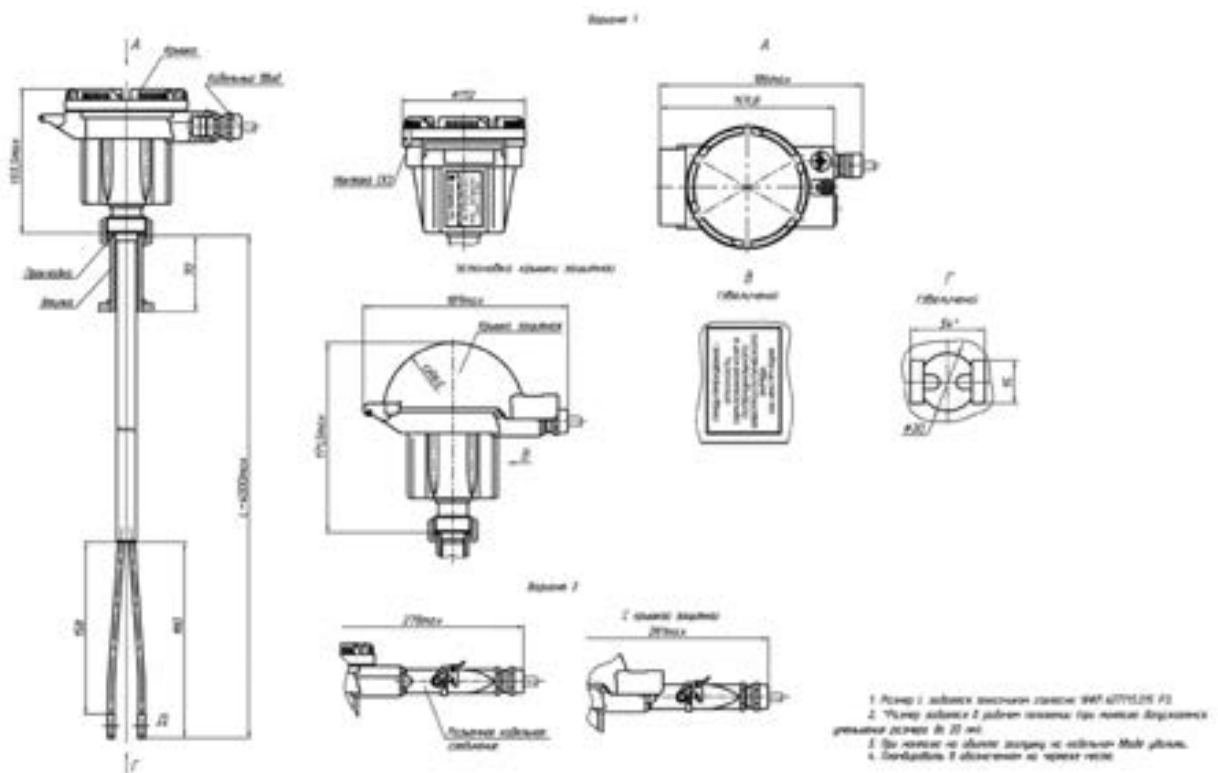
Габаритные размеры датчика ДПУ5А
